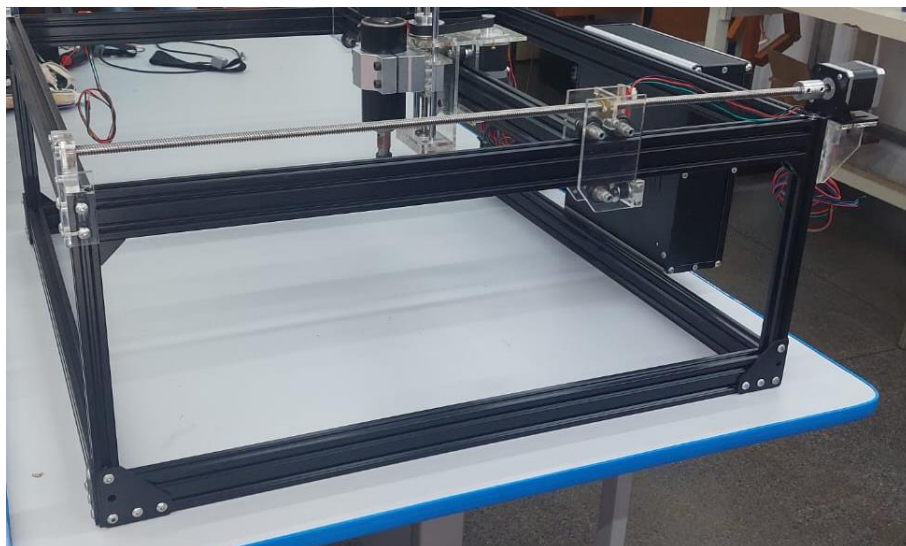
Partes A, B e C do conjunto de movimentação do eixo Y (Y2) montadas
